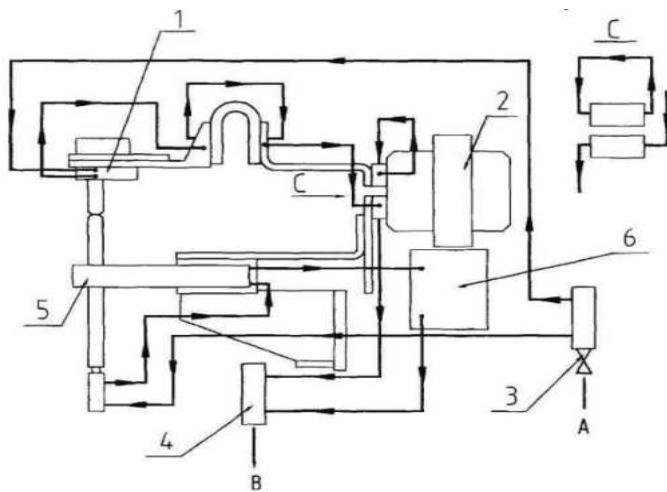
Схема охлаждения машины контактной точечной сварки МТ-1928
